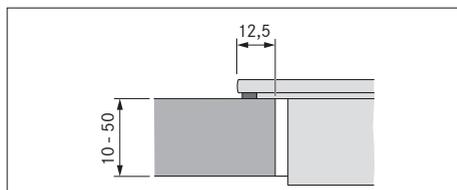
Dimensioni di appoggio per montaggio sopra piano
